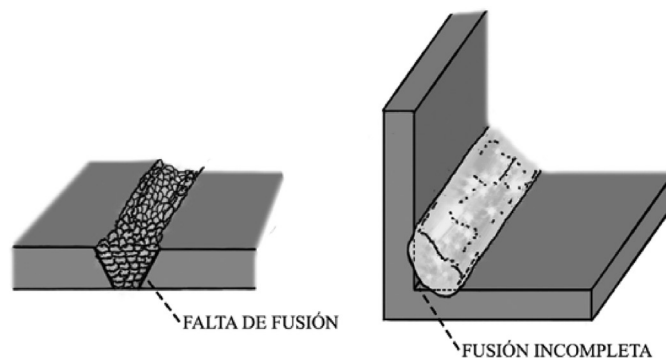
Defectos en la soldadura: fusión incompleta
